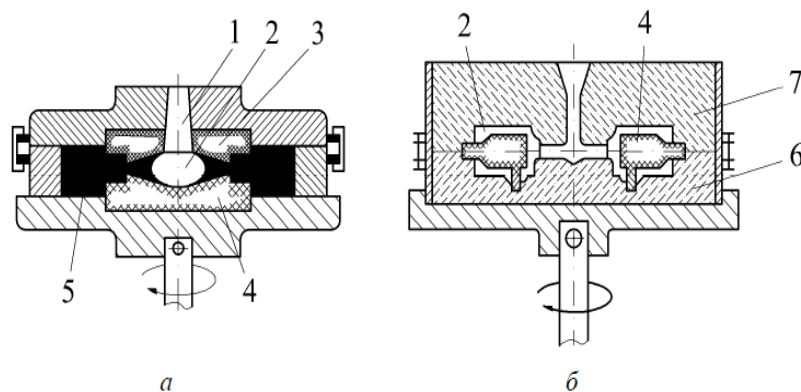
Схема получения фасонных отливок: а - венцов шестерен; б - мелких фасонных отливок; 1 - стояк; 2 - рабочая полость; 3, 4 - стержни; 5 - избыток расплава (сверх массы отливки); 6 - нижняя полуформа; 7 - верхняя полуформа
